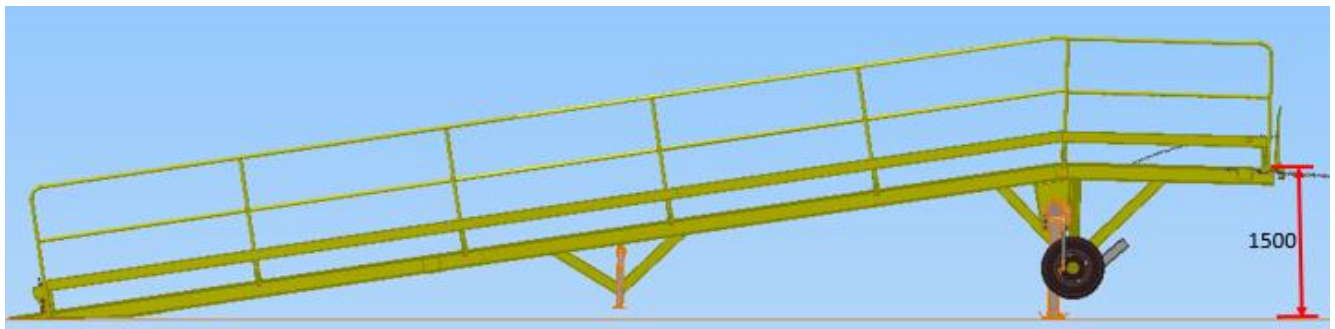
Vista completa - elevação com aparelho de levantamento sem o uso do prolongador.
